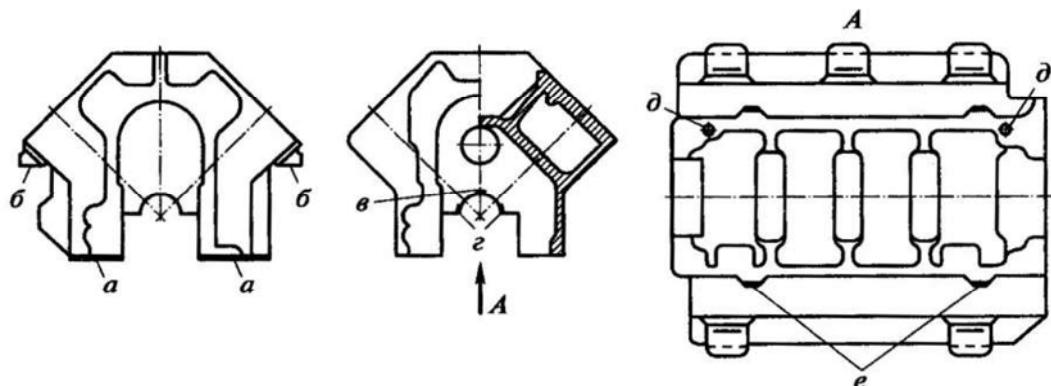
Расположение установочных поверхностей (а—е) на заготовке V-образного блока цилиндров
